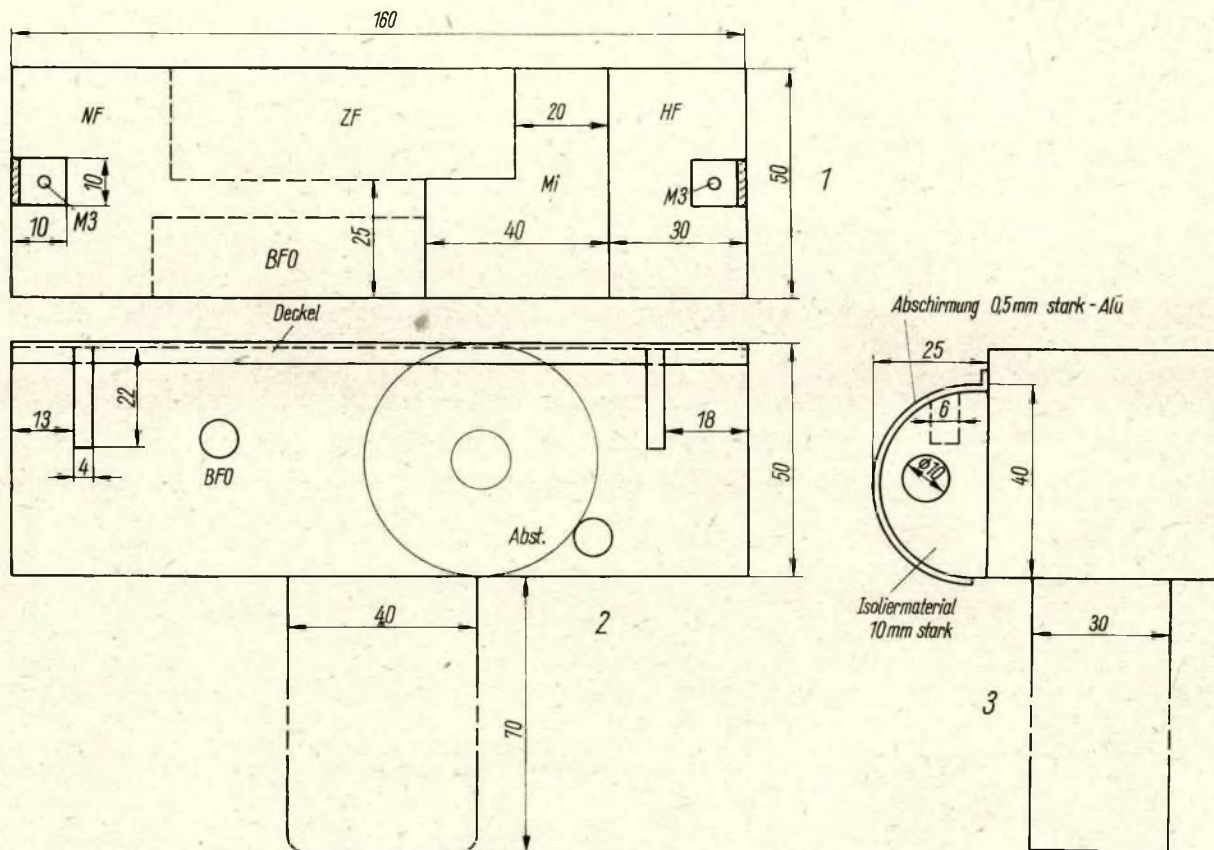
bis 3: Maßskizzen für das Gehäuse des Peilsupers (1 - Draufsicht, 2 - Vorderansicht, 3 - Seitenansicht)
